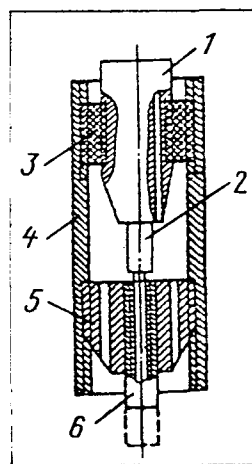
Устройство для сварки с увеличенным вылетом:
